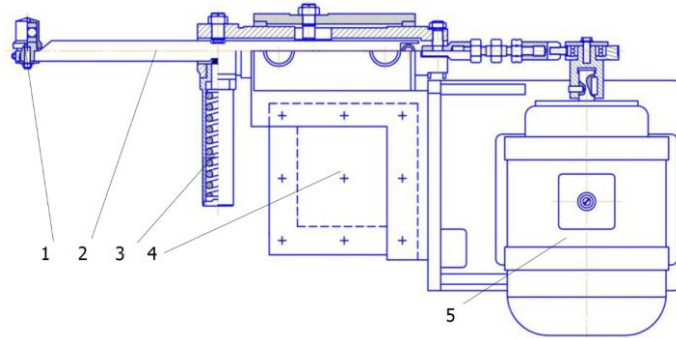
Універсальний пристрій для розкочування циліндрових втулок:
